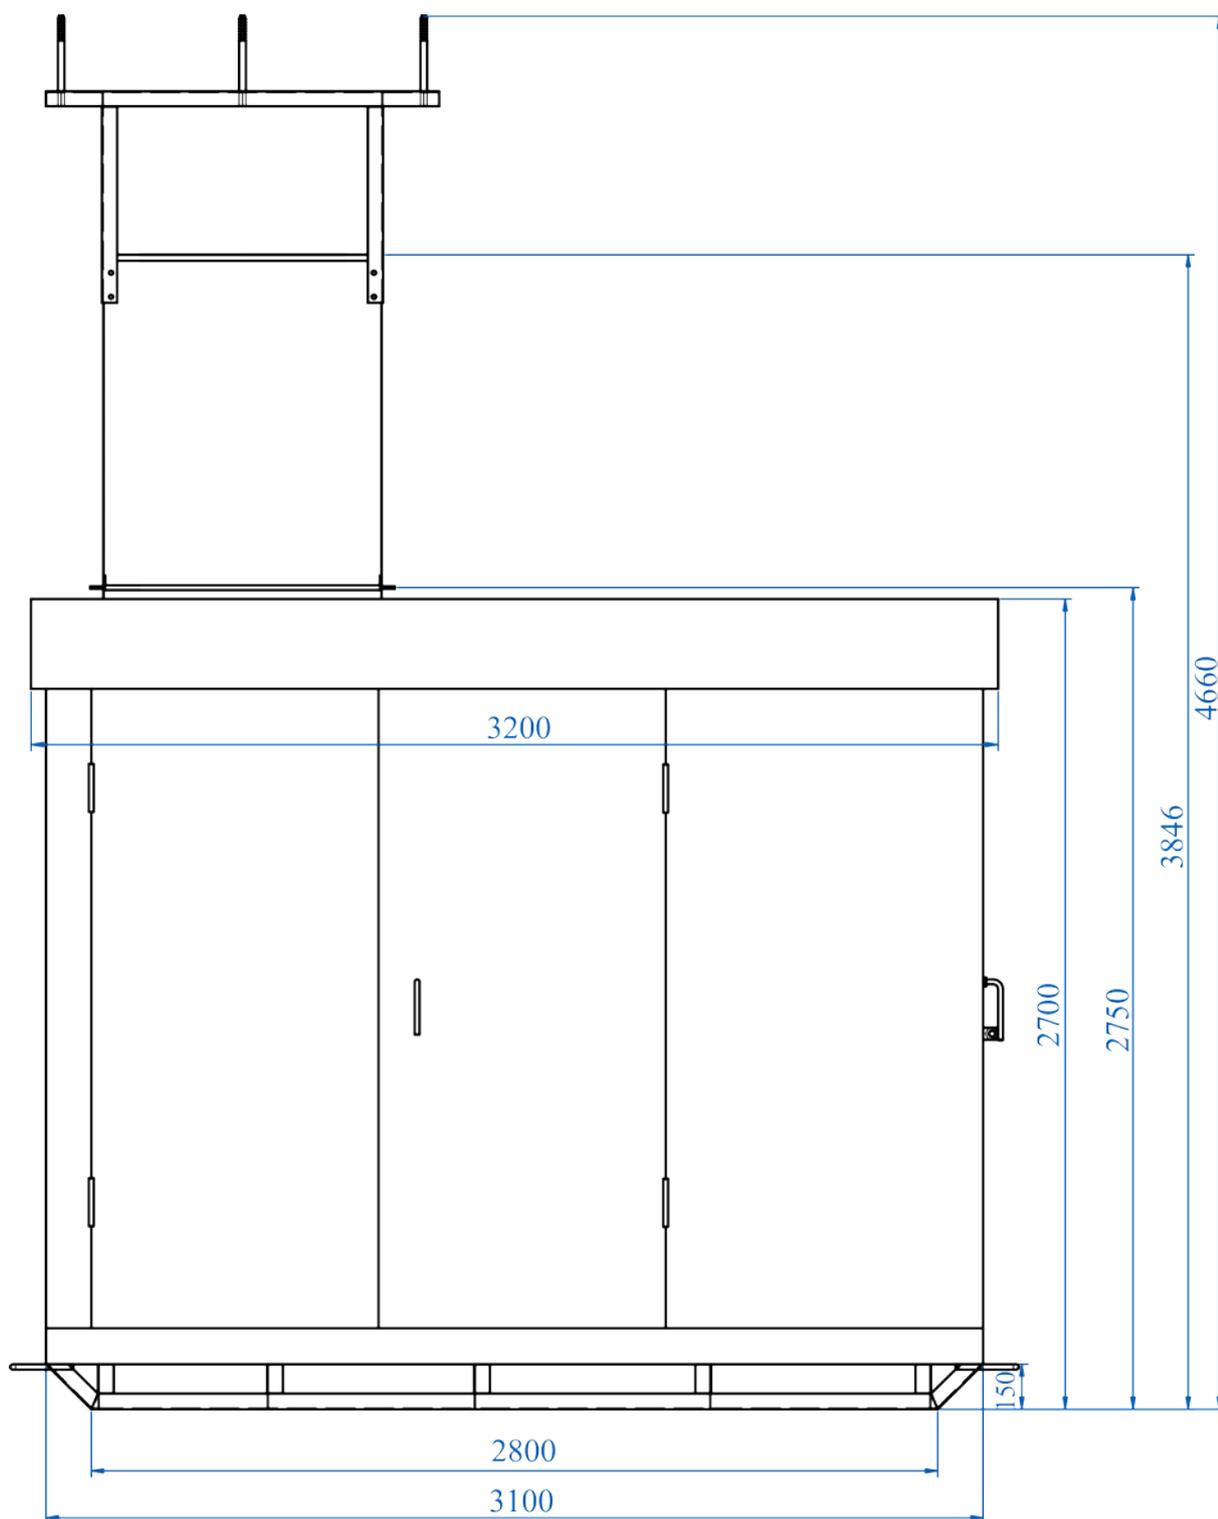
Внешний вид и габаритные размеры КТПН – 250, 400, 630 кВА
